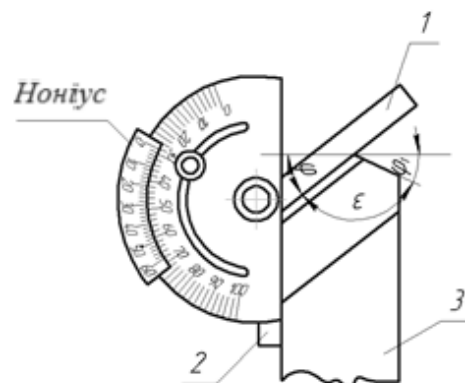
Вимірювання кута φ токарного прохідного різця
